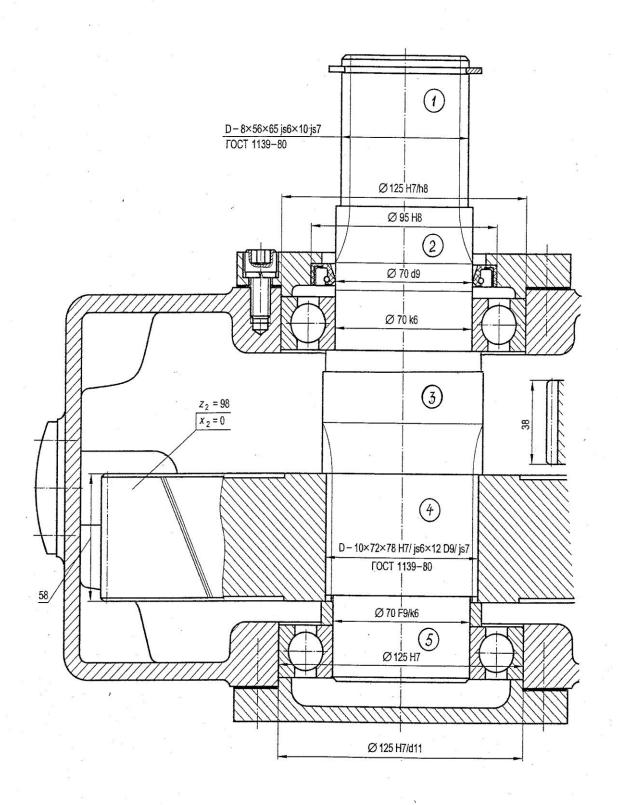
Тихоходный вал редуктора со шлицами и одним насадным цилиндрическим зубчатым колесом тихоходной ступени [I] (к примеру 2.4)
